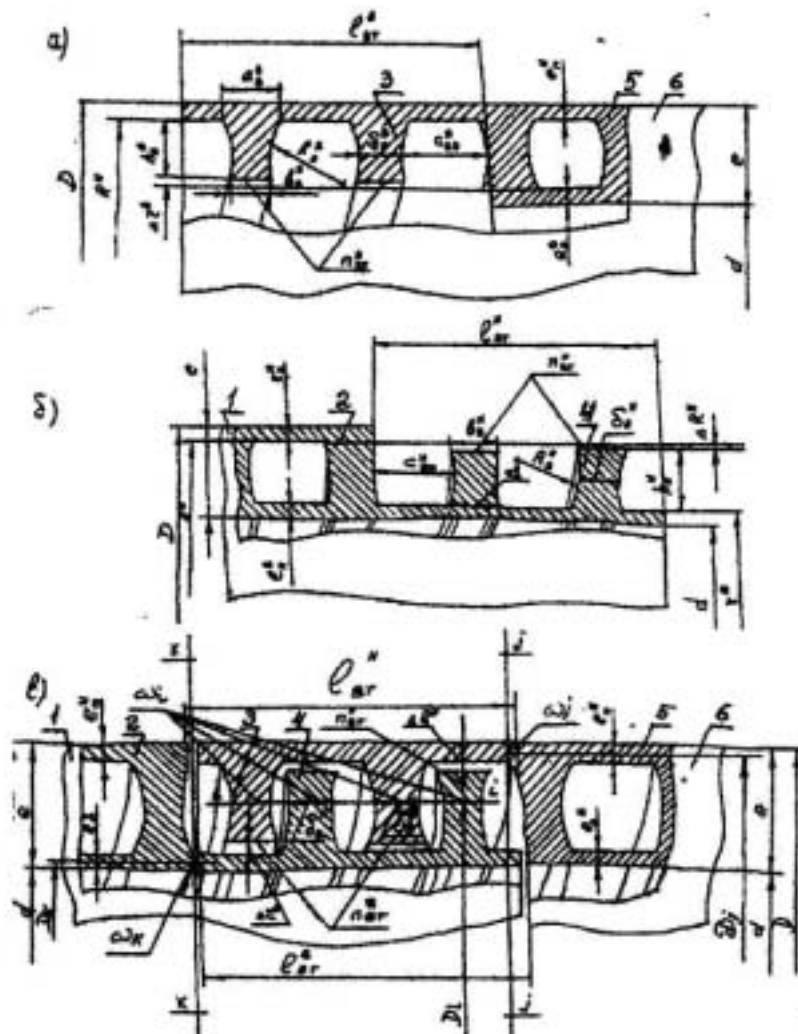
Винтовое соединение ВПСТ труб из ПНД между собой по схеме «цилиндр в цилиндр»
